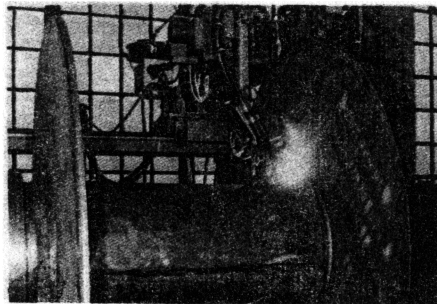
Doppelkopfschweißroboter im Einsatz
